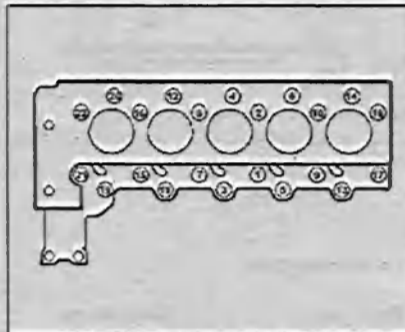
Порядок затягивания болтов крепления головки блока цилиндров.
